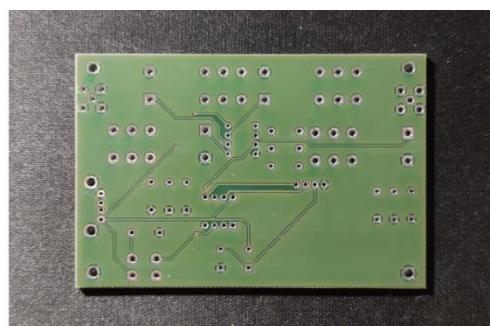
PCB πλακέτα 3D (side)
